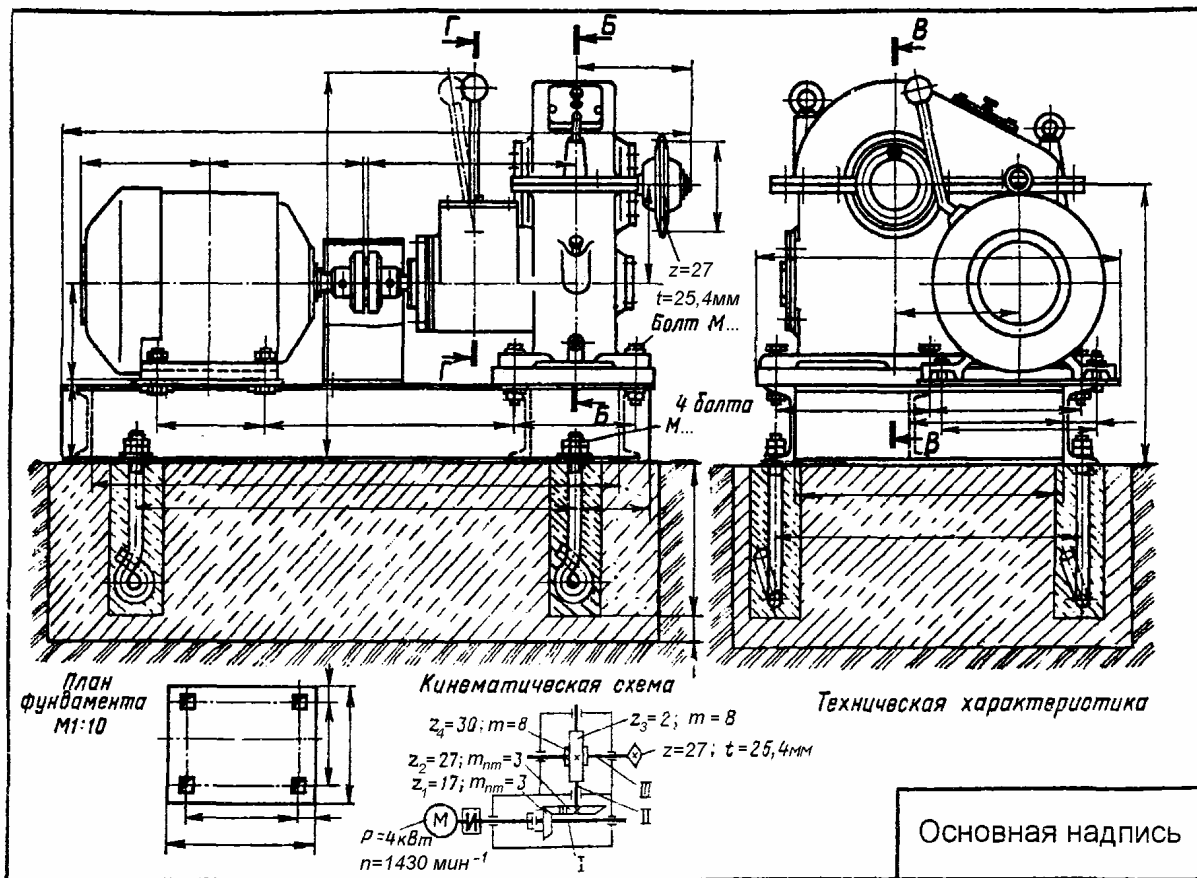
Общий вид привода с установкой на сварной раме
